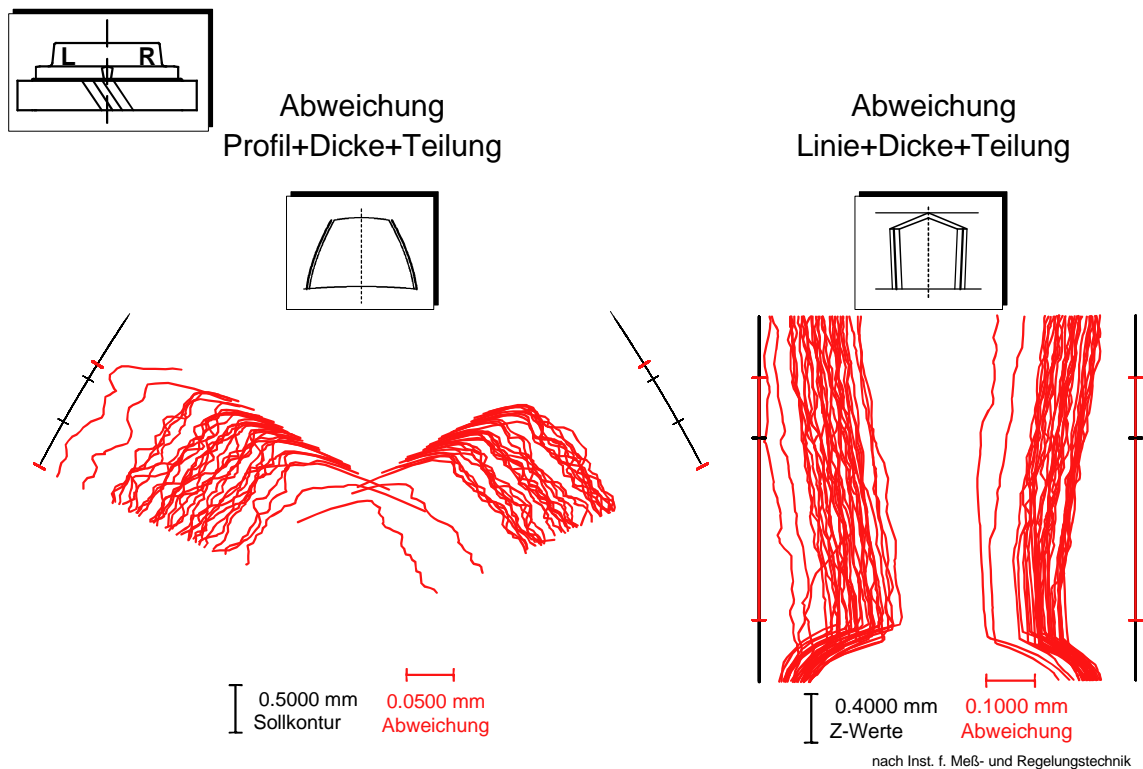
Messwerte der hinterschnittenen Kupplungsverzahnung mit maschinenseitigem Anschlag
